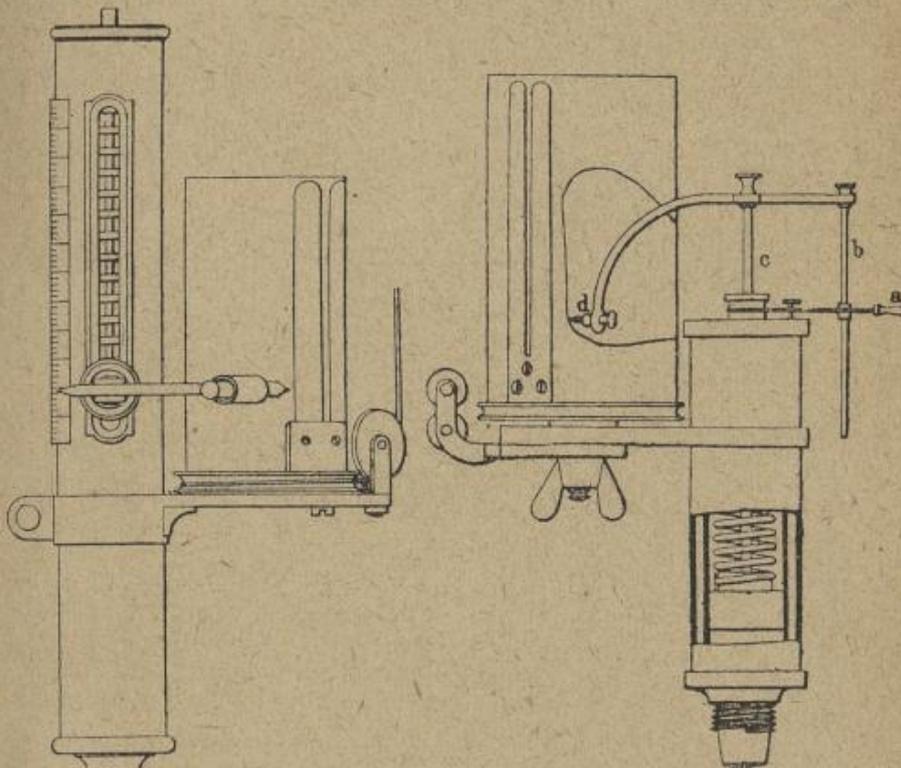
Indicateur à barillet d'Hopkinson (d'après le guide pour l'essai des machines de Buchetti).
